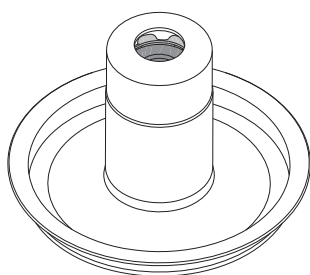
Корпус ротора с держателем подшипника и керамической втулкой подшипника
